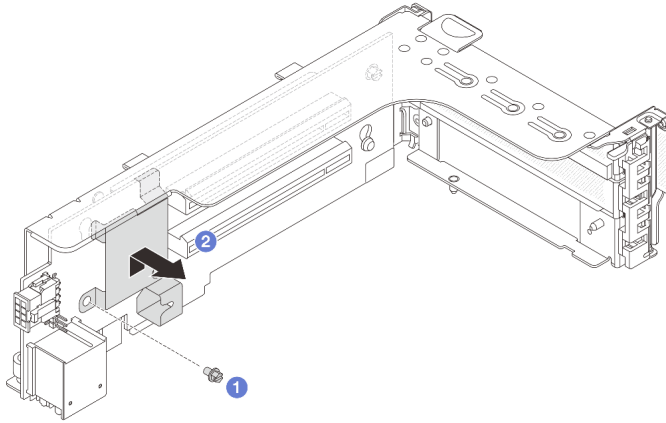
Entfernen des Befestigungsclips an der 7-mm-Laufwerkhalterung
